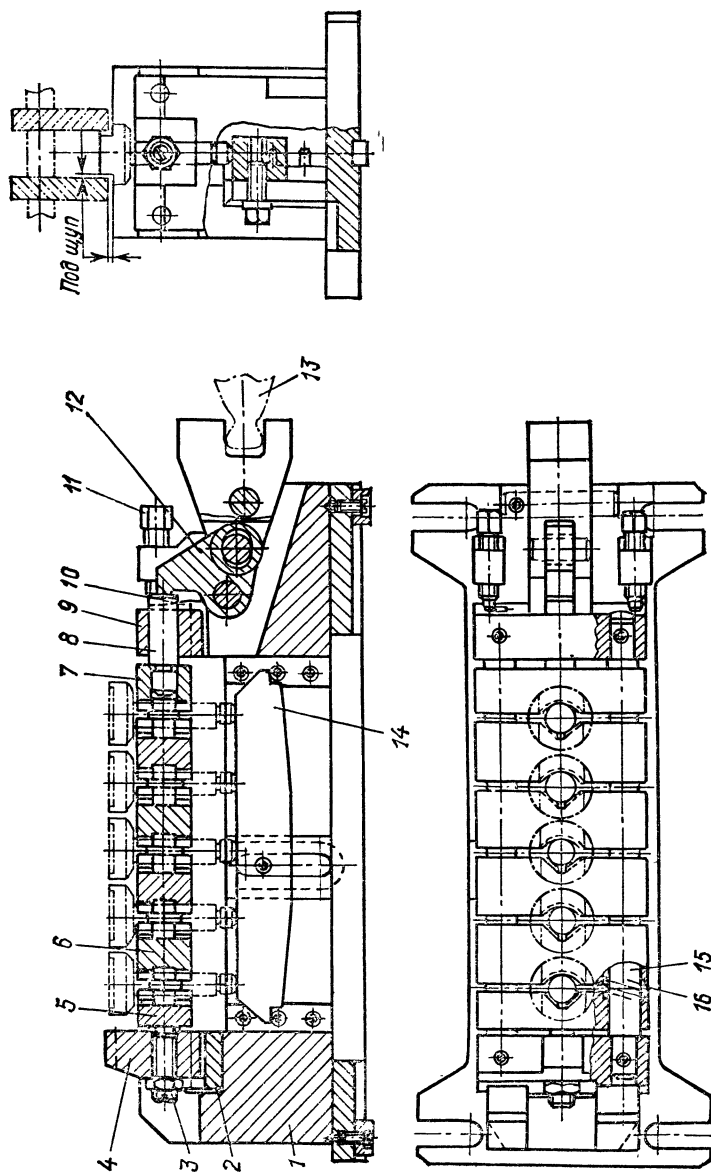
Специализированное наладочное приспособление со скальчатыми кассетами для фрезерования деталей типа валов и втулок
